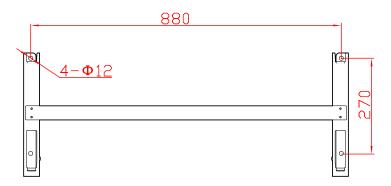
Dimensione dei fori di installazione (unità di misura: mm)
